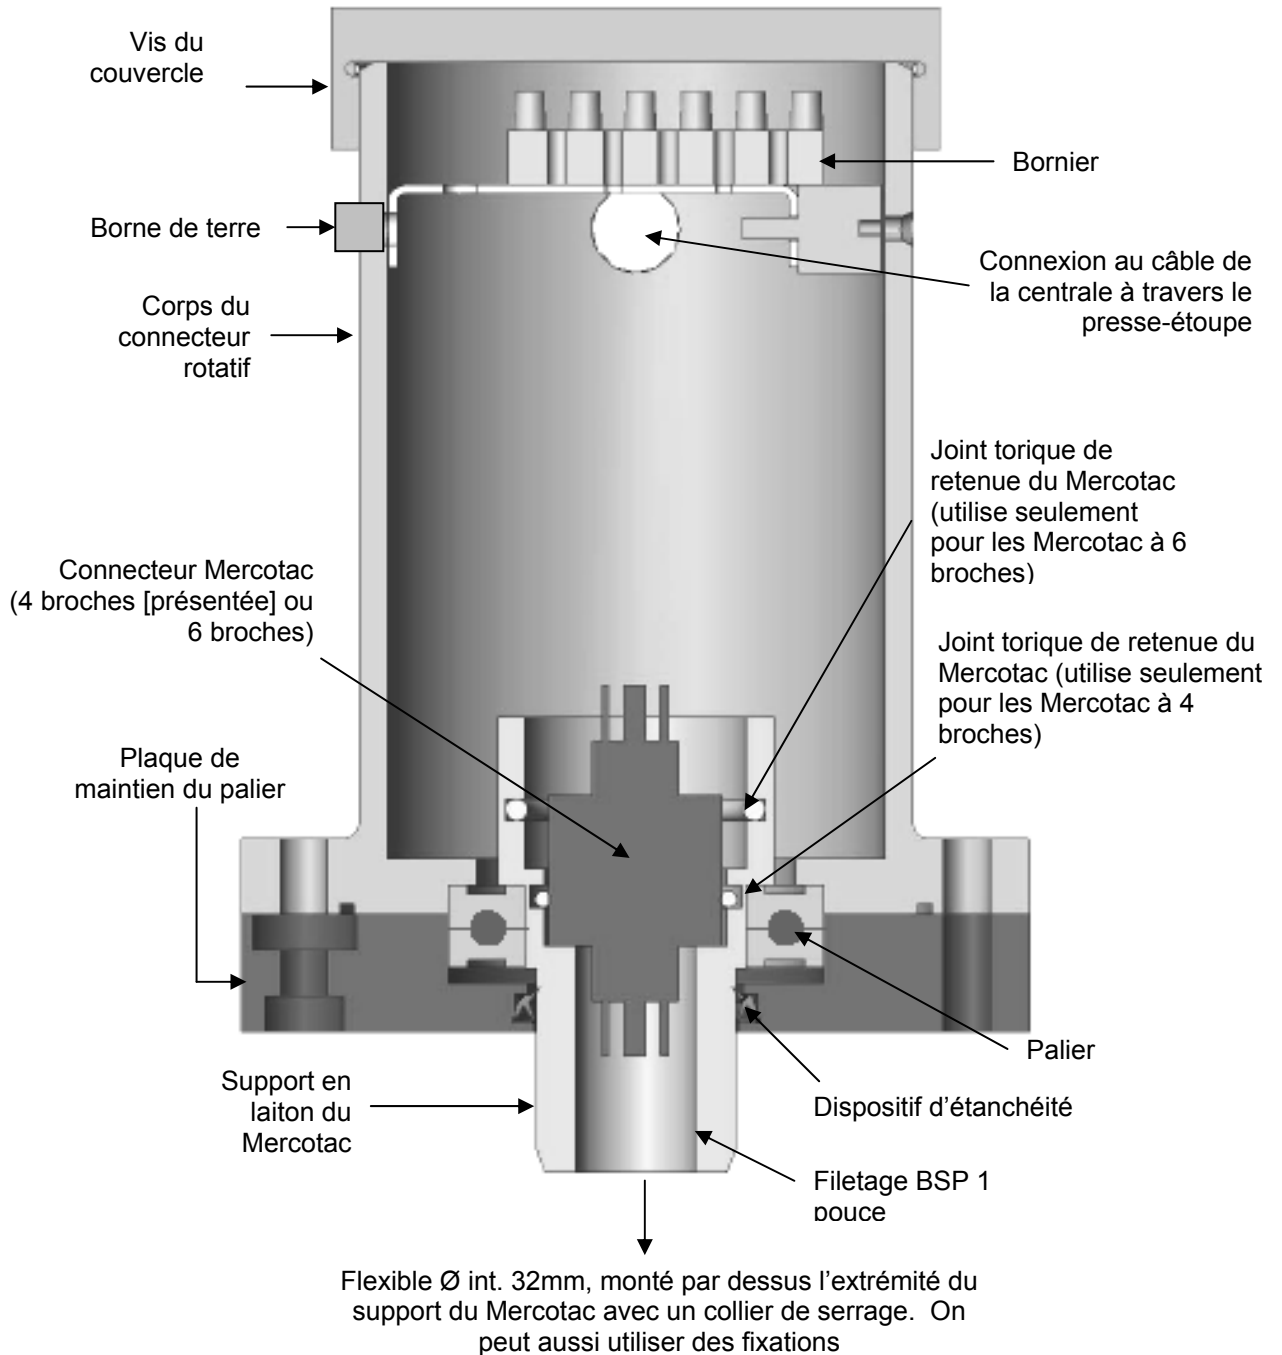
Assemblage de connecteur rotatif de type 'B'
